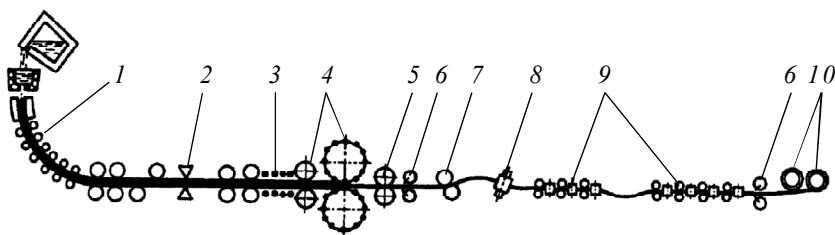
Схема литейно-прокатного агрегата для производства стальной проволоки:
